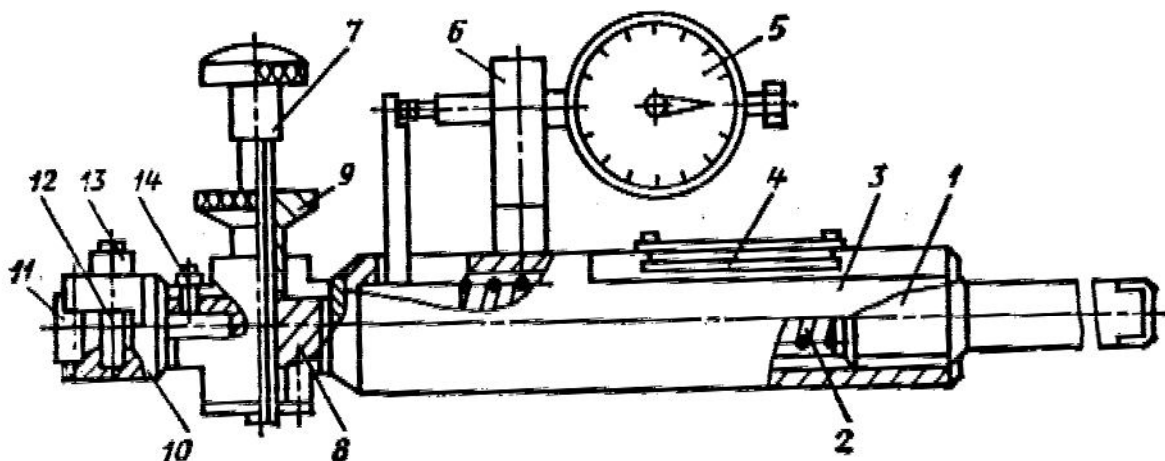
Державка для выглаживания роликом: 1—винт пружины; 2—пружина; 3—корпус державки; 4—шкала; 5—индикатор часового типа; 6—стойка; 7—винт стопорный; 8—переходник; 9—контргайка; 10—головка; 11—ролик; 12—шпилька; 13—стяжная гайка
